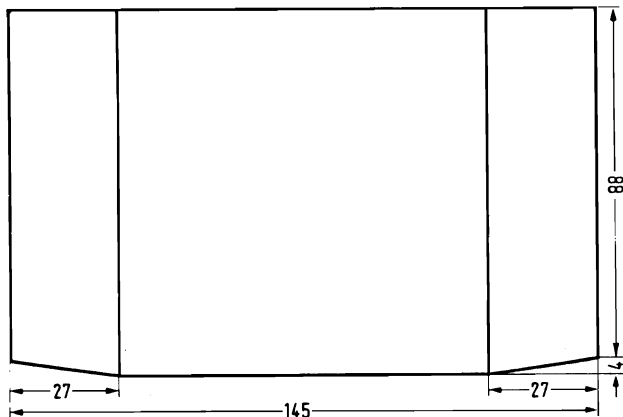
Maßangaben für das Gehäuse des Mustergerätes (in mm)
